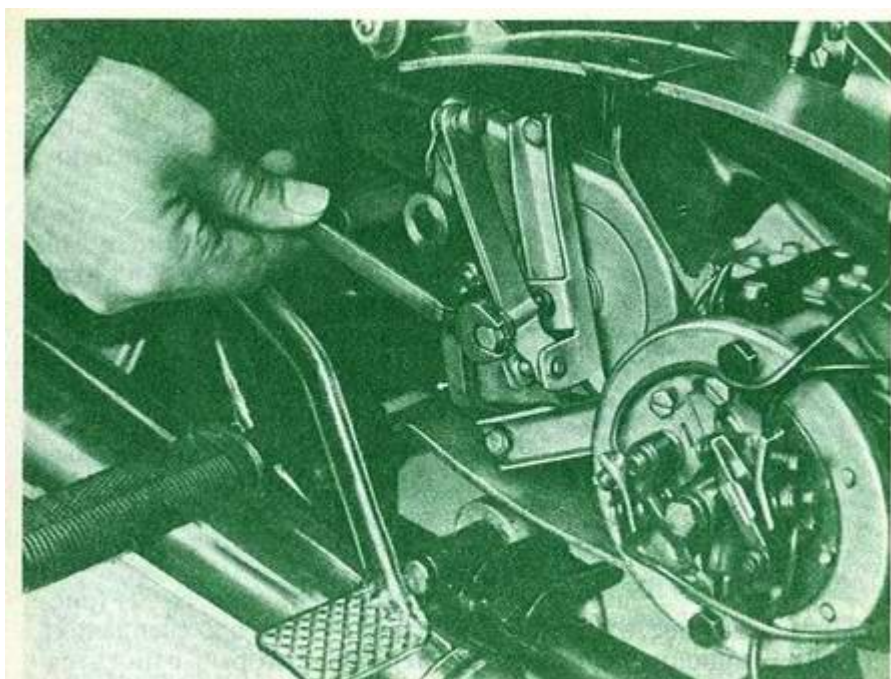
Механизм выключения сцепления двигателя мотоцикла мод. 634 и его регулировка
